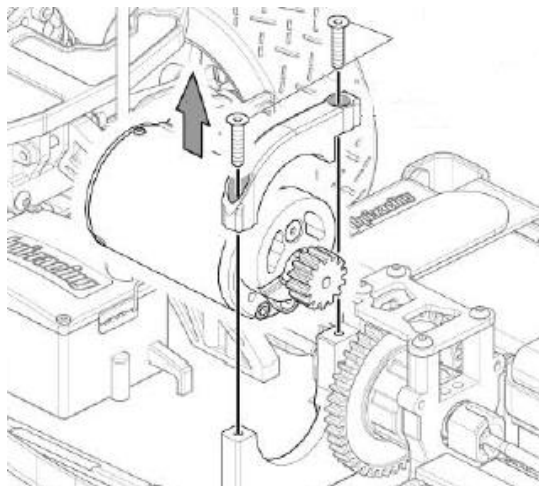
Механическая связь центрального дифференциала и вала двигателя
